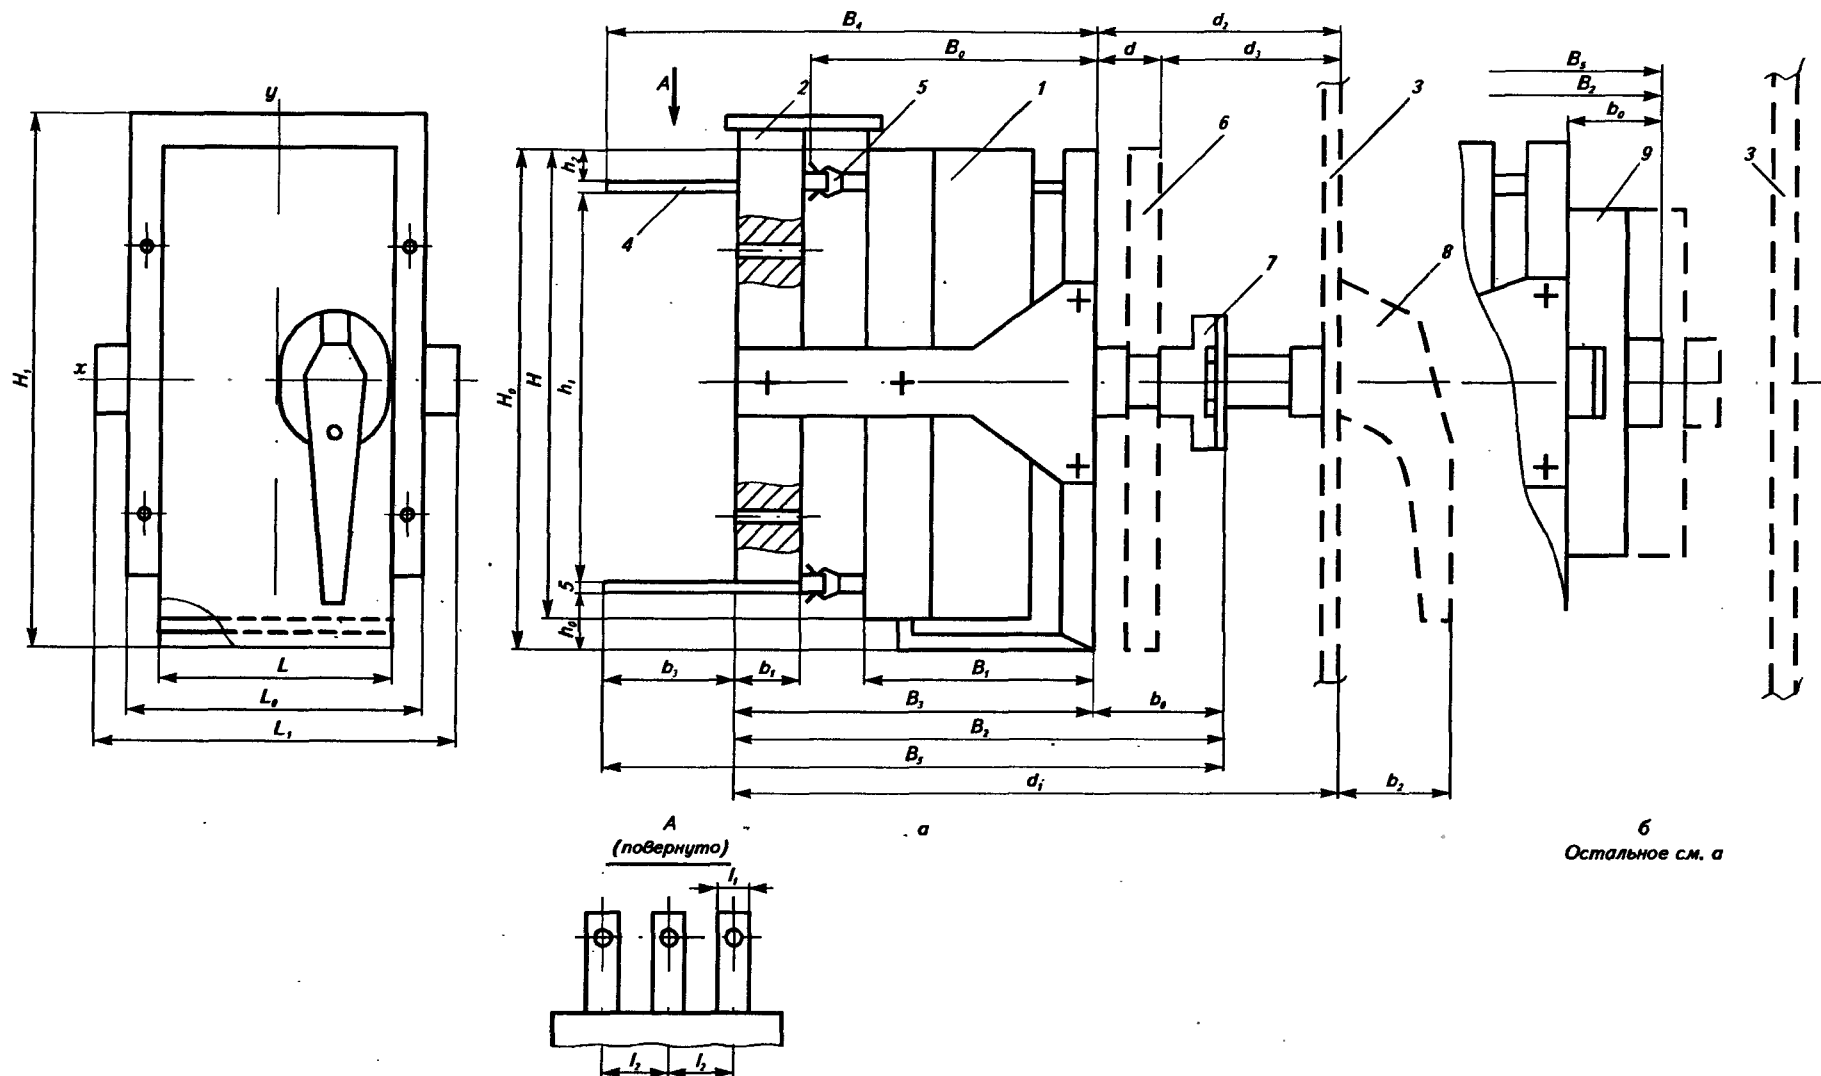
Габаритный чертеж выключателей выдвижного исполнения с механической блокировкой с ручным или электромагнитным приводом (вариант I)
